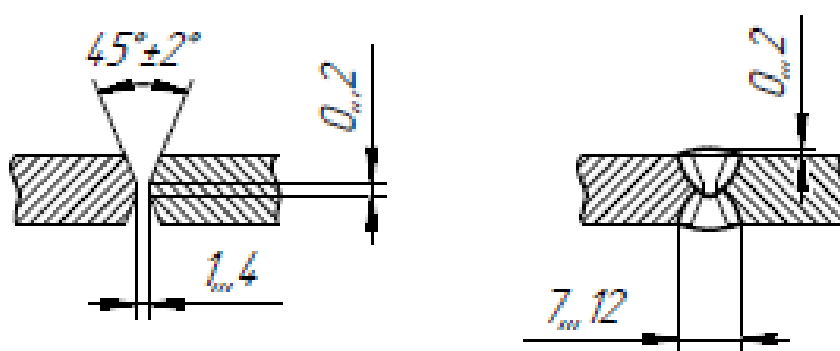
Геометрия вертикального сварного шва
